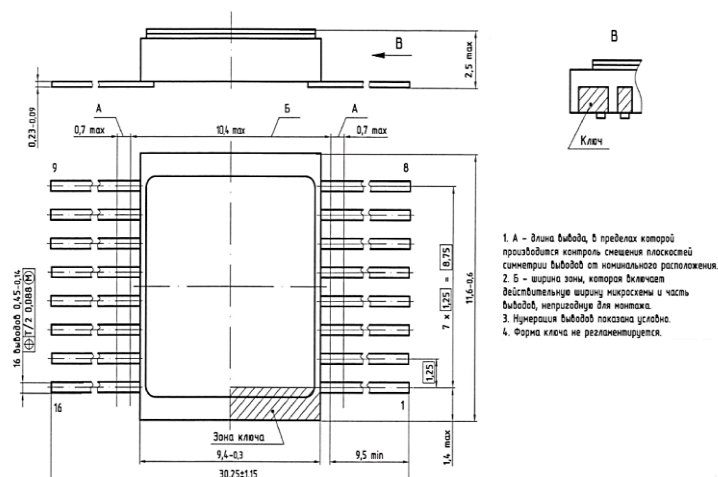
Габаритный чертеж корпуса 402.16-18 (размеры в мм)
